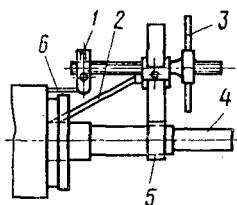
Приспособление для извлечения стержней из пазов ротора
